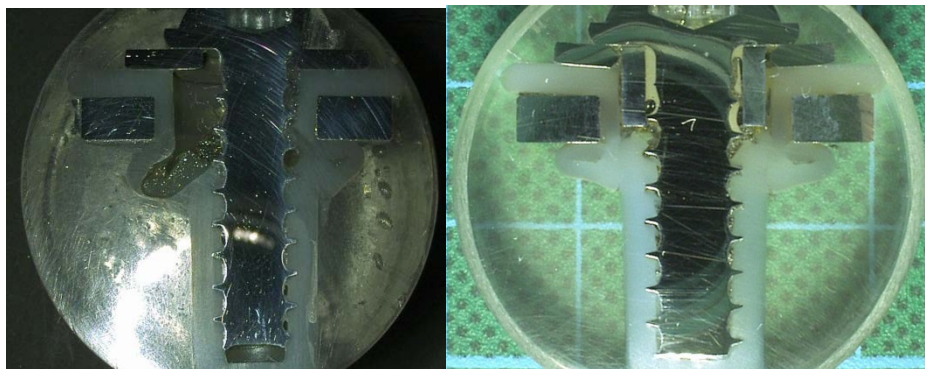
Schliffbild verschraubter Probekörper ($\varphi = 1440$; $M_A = 2,5 \text{ Nm}$; $n_2 = 50 \text{ min}^{-1}$); links: EJOT Delta PT Schraube; rechts: modifizierte Schraube
